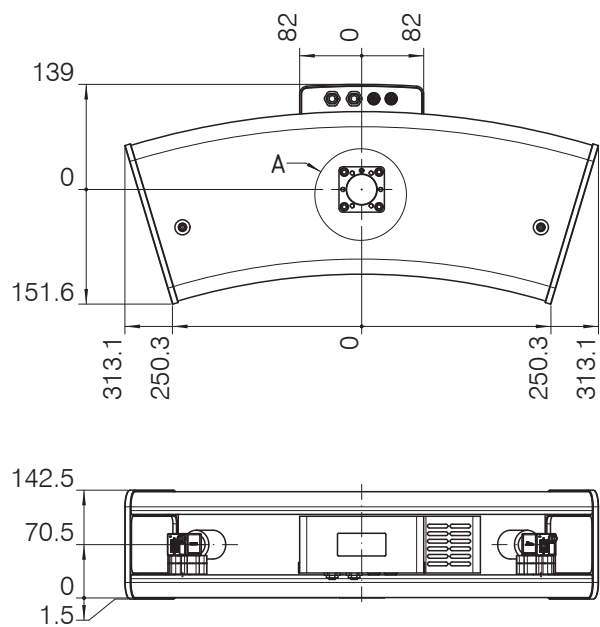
Maßzeichnung Sensor surfaceCONTROL 3D SC25x0
